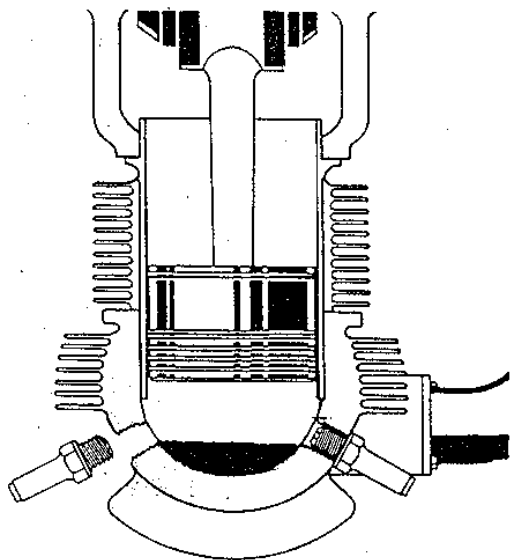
Drenagem de um composto preventivo da corrosão.
